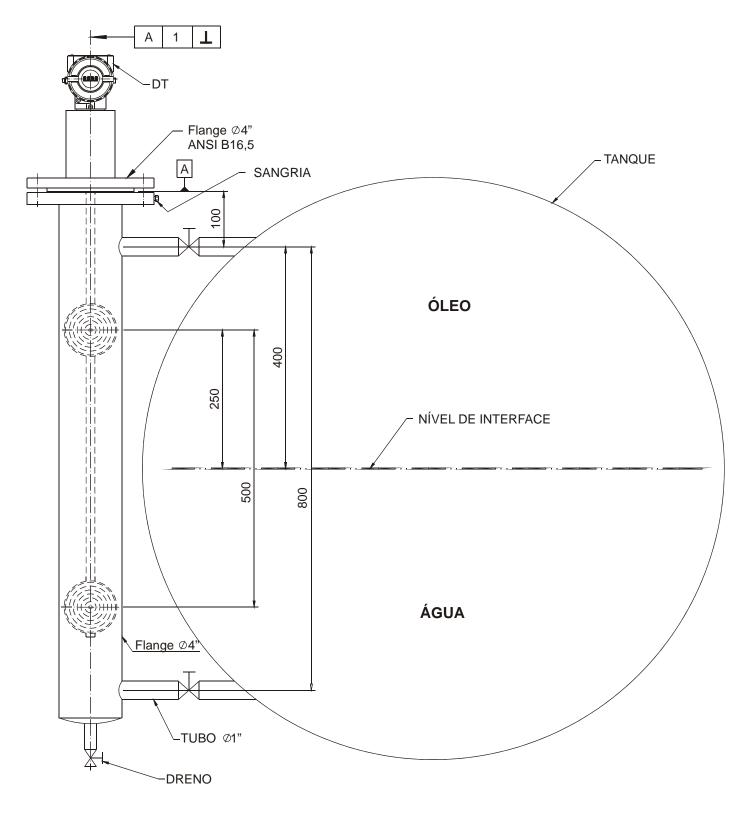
Tipos de Instalação para o DT302 (J)
